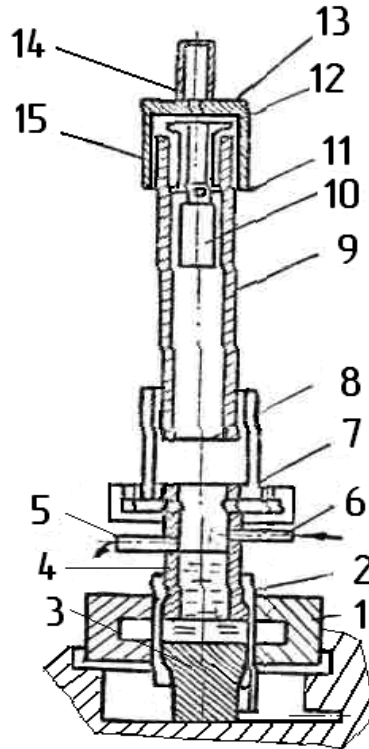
Схема пристрою для штампуванні на пресс-гарматі
